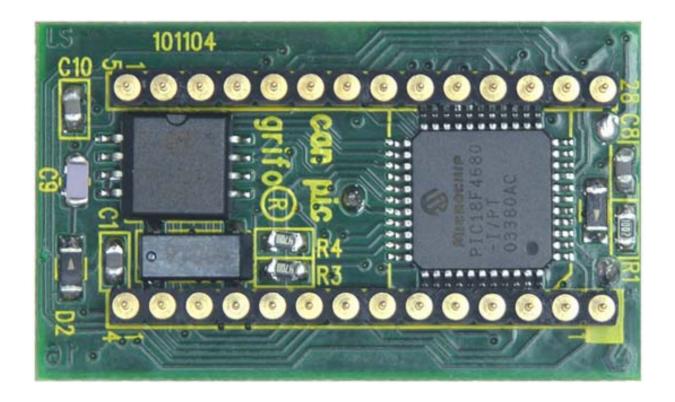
VISTA DAL BASSO DELLA CAN PIC
